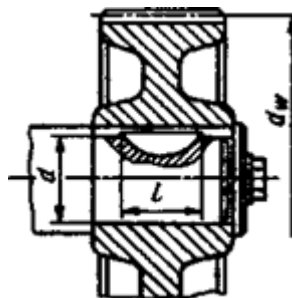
Шпоночное соединение зубчатого колеса с валом
